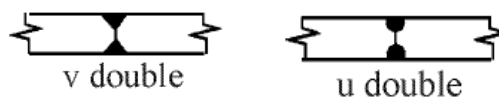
soudure en bout à pénétration partielle.
